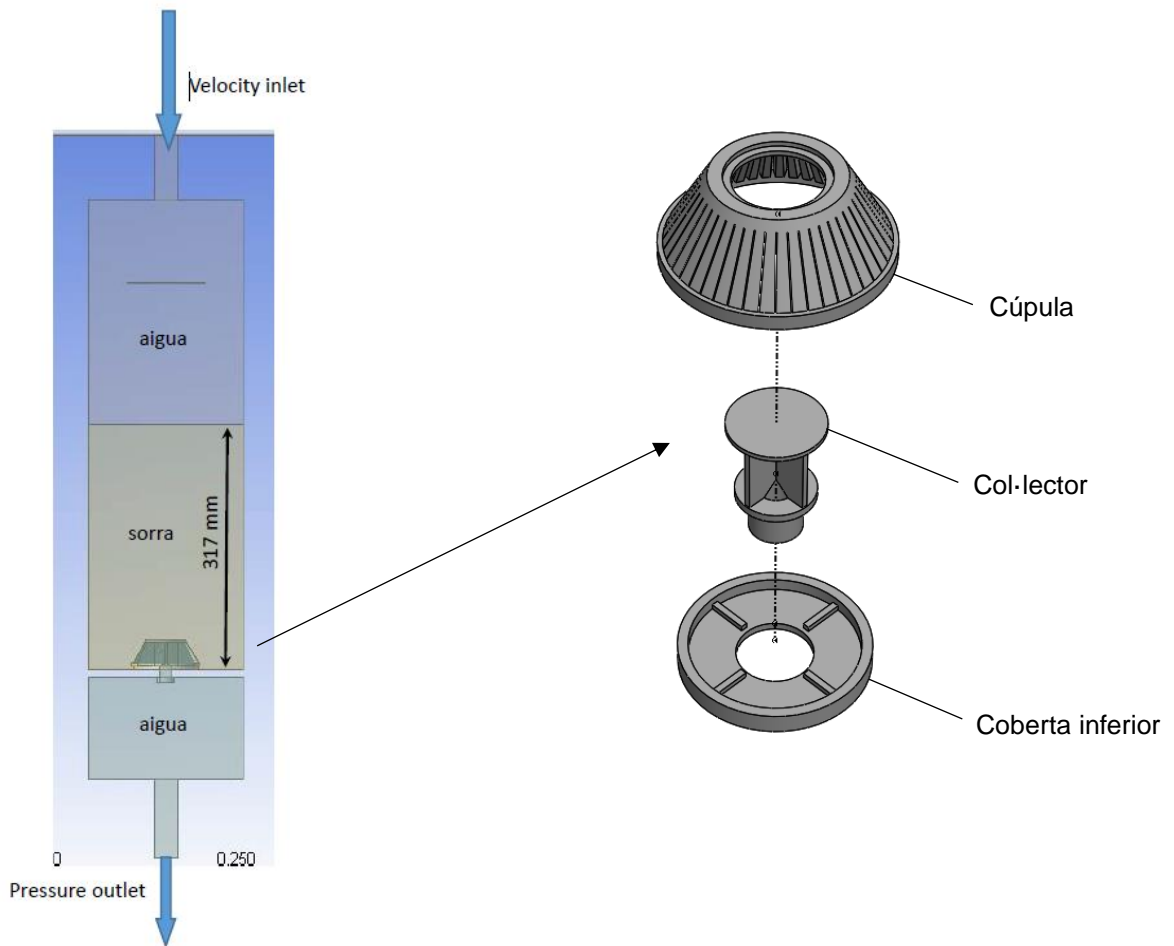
Detall amb la vista explosionada de la crepina comercial (dimensions en mm)
